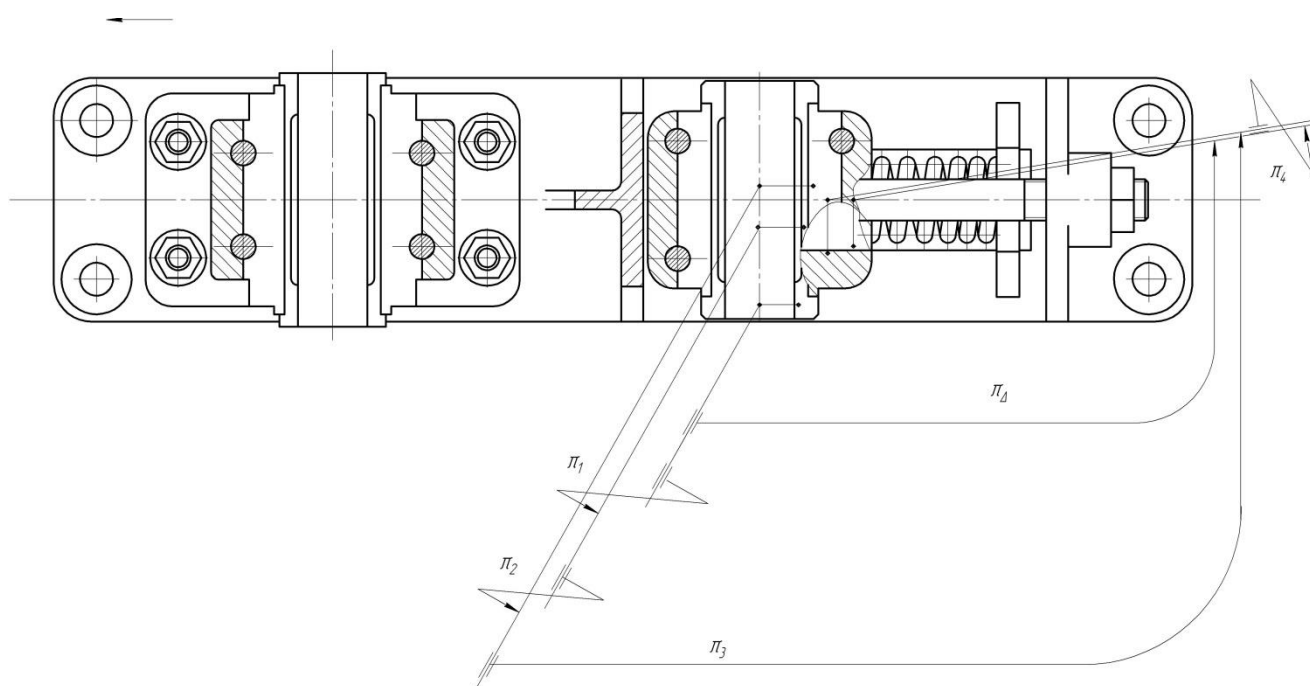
Розмірний ланцюг π , який забезпечує плавне переміщення корпусу 4
